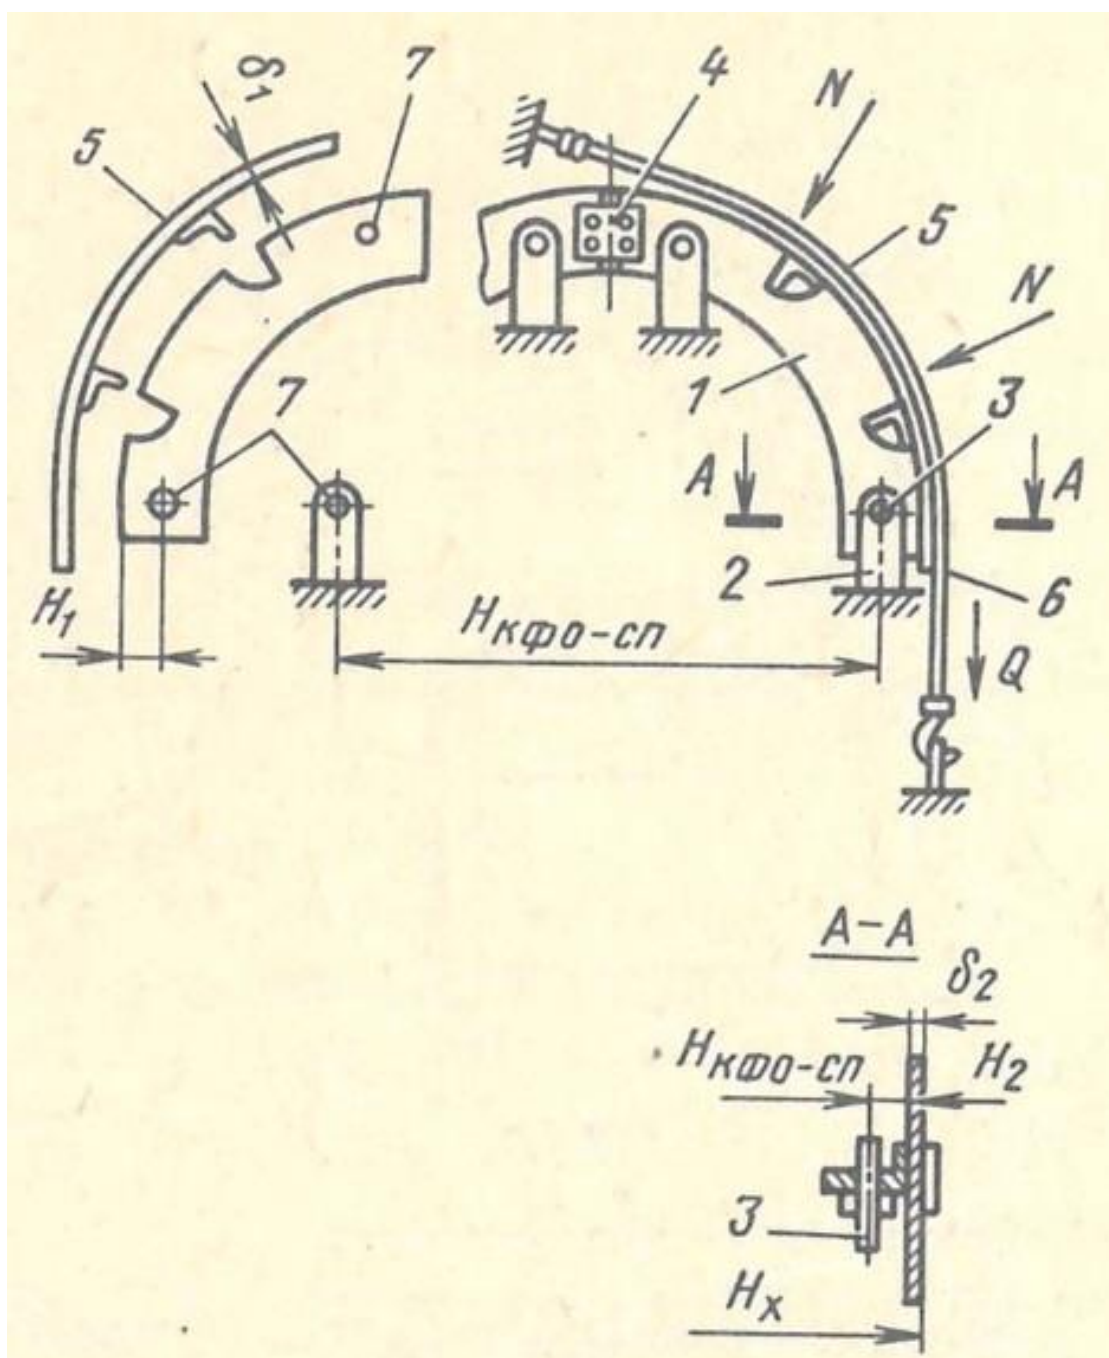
Схема базирования по КФО шпангоута: 1 – обод шпангоута; 2 – вилка СП; 3 – фиксатор; 4 – компенсатор; 5 – обшивка со стрингерным набором; 6 – прижим; 7 – КФО.
